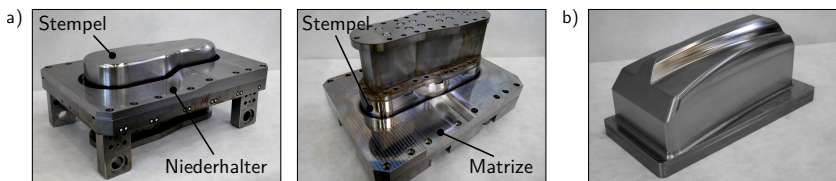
a) Tiefziehwerkzeug bestehend aus Stempel, Niederhalter und beschichteter Matrize. b) Stempel eines Tiefziehwerkzeugs in Anlehnung an ein Werkzeug zur Herstellung einer B-Säule aus einem Personenkraftwagen.
